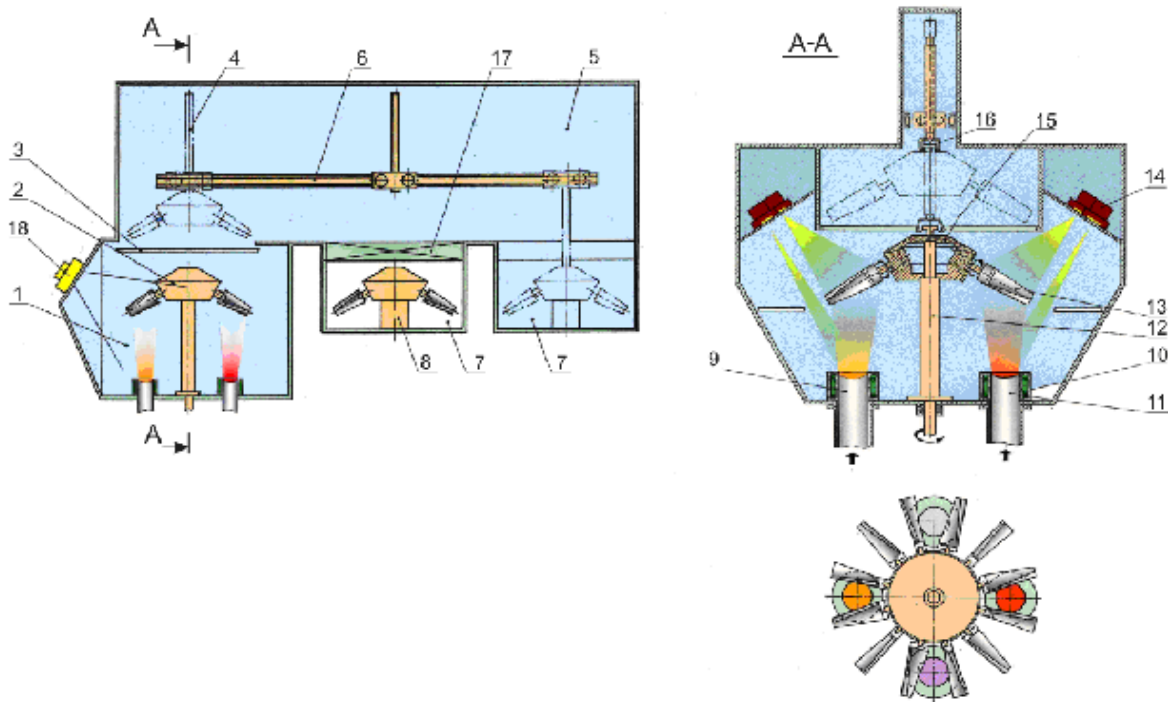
Общий вид установки и схема нанесения покрытий: 1 – рабочая камера; 2 – планетарный механизм вращения изделия (лопаток); 3 – заслонка; 4 – манипулятор; 5 – переходная камера; 6 – рельсы; 7 – шлюзовые камеры; 8 – подставка; 9 – керамический слиток; 10 – металлический слиток; 11 – тигель; 12 – вращающаяся опора; 13 – изделие (лопатка); 14 – электронная пушка; 15 – приводная шестерня; 16 – захват; 17 – затвор
